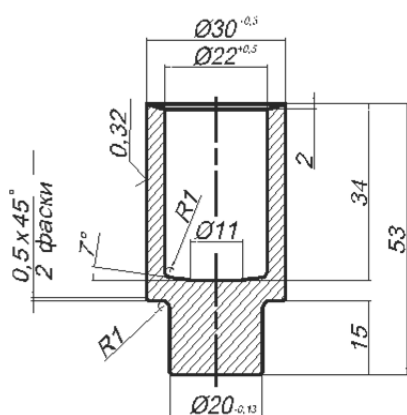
Чертеж детали «поршень тормозного цилиндра»
